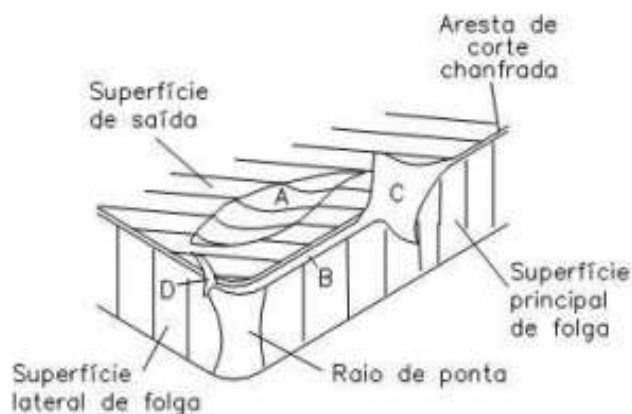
Tipos de desgastes em ferramenta de corte: (A) Desgaste de cratera; (B) Desgaste de flanco; (C) e (D) Desgaste de entalhe (Machado *et al.*, 2011).
